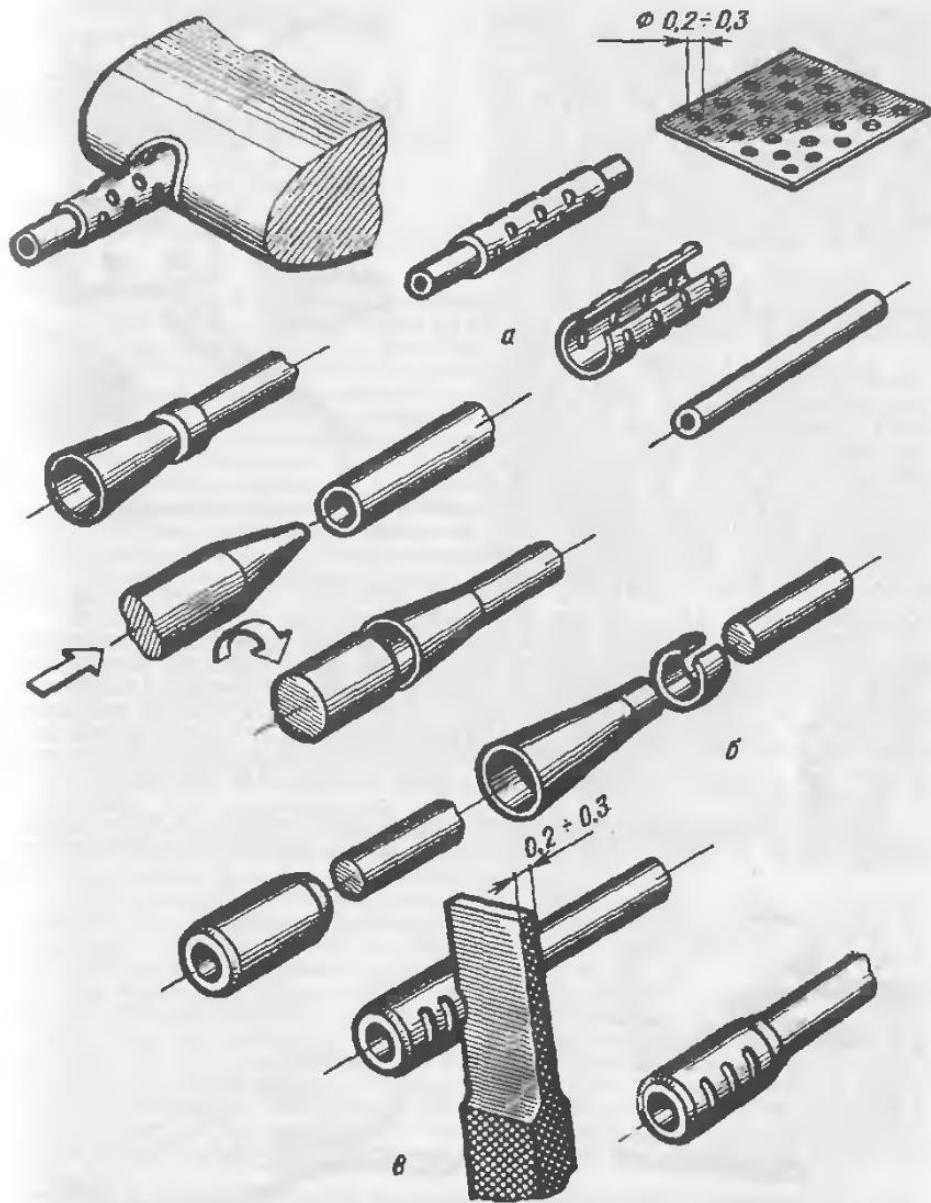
Изготовление выступающих частей стрелкового оружия: а - с перфорированным кожухом; б - с пламегасителем; в - с дульным тормозом
